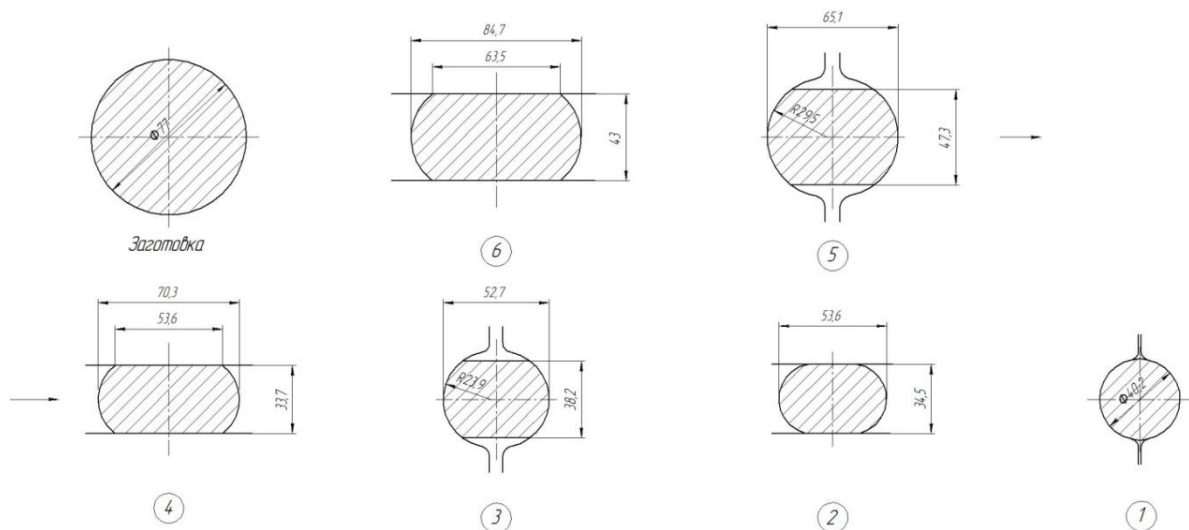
Калибровка валков чистовой группы клетей стана 390 для прокатки круглой стали диаметром 40 мм
